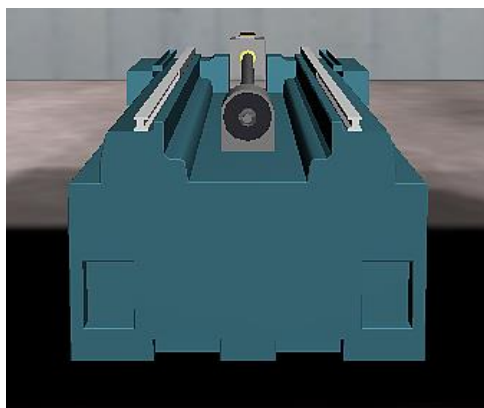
Вид станка вид при снятых кабинете, кожухах инструментального магазина и шпиндельной бабки и при отсутствии бака для СОЖ [24]:
